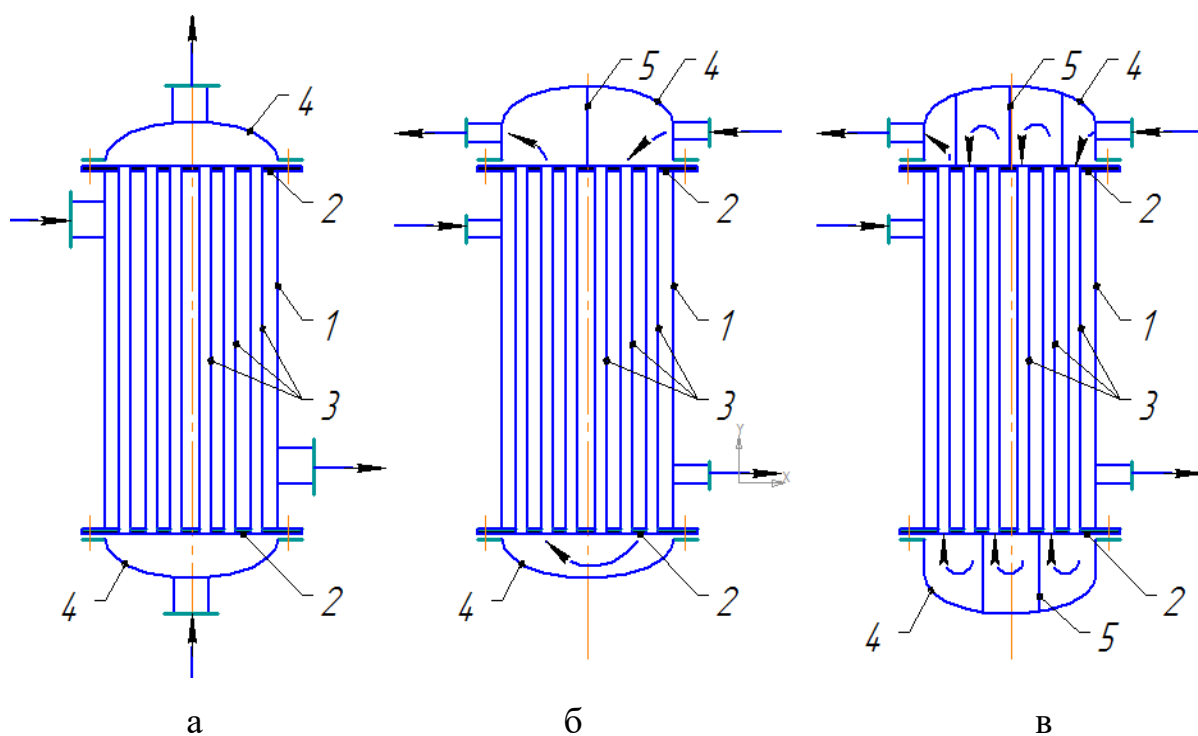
Кожухотрубчатые теплообменники с неподвижными решетками: а – одноходовой; б – двухходовой; в – шестиходовой: 1 – корпус; 2 – трубные решетки; 3 – трубы; 4 – крышки; 5 – перегородки
